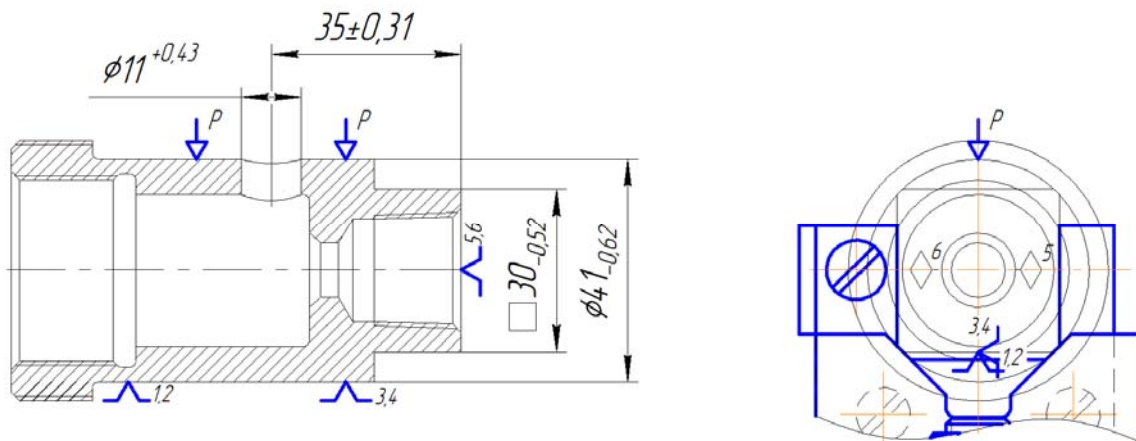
Схема базування деталі «Корпус» 26.KBP.400.11.00.000 в пристосуванні
